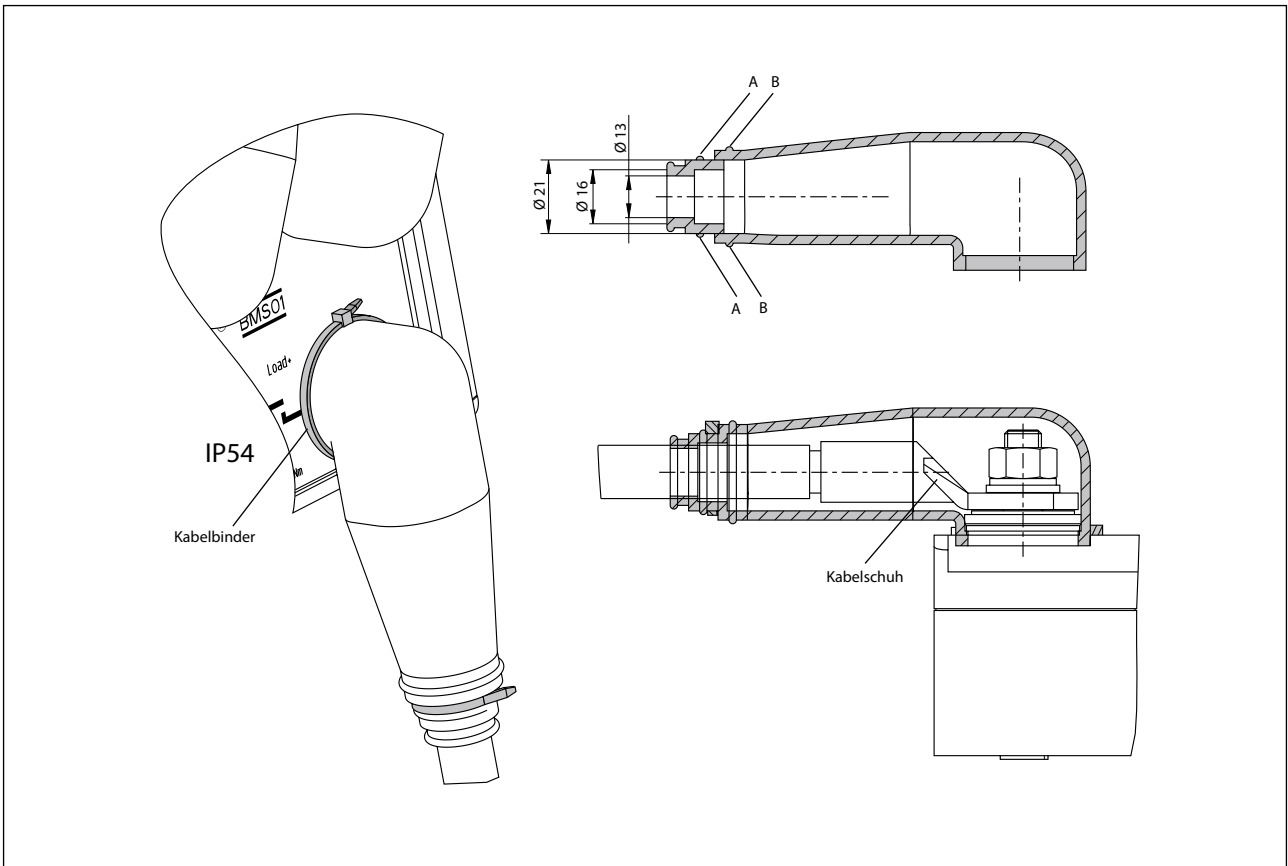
Kabelbefestigung an Schraubanschluss des BMS01
